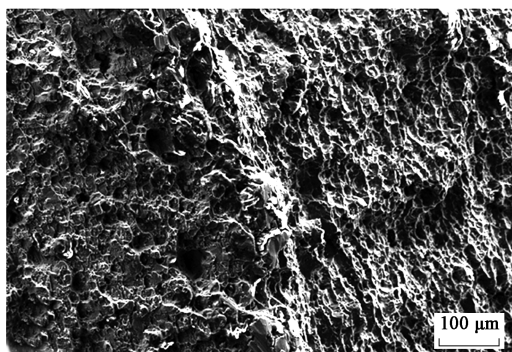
辊弯 V 型件断裂部位的断口形貌
